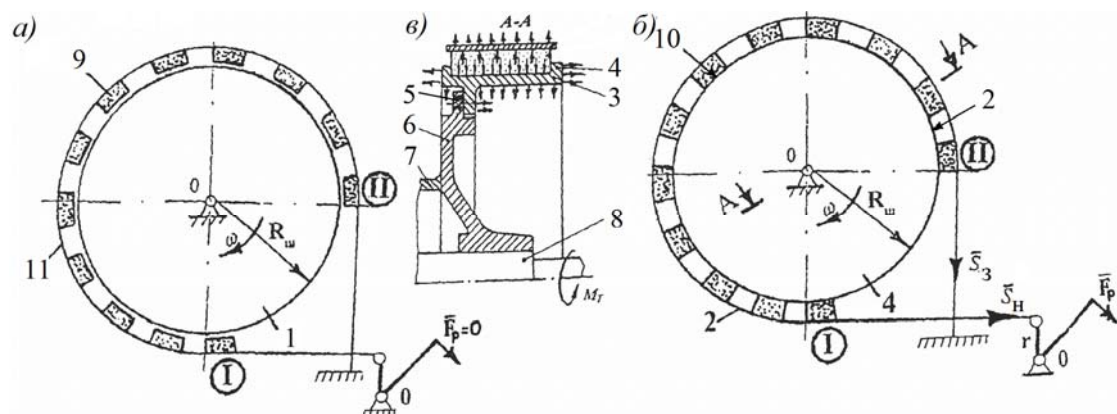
а, б, в – Кінематична схема серійного СКГ з розімкненими (а) і замкнутими (б) ФВ (в): 1, 2, 3, 4, 5 – ГШ, робоча і неробоча поверхні ободу, реборди і кріпильний виступ; 6, 7 – фланець барабана; 8 – підйомний вал; 9, 10 – ФН з робочою поверхнею; 11 – ГС з набігаючою (I) і збігаючою (II) гілками; S_H , S_3 – натяги набігаючої і збігаючої гілок ГС; M_T – гальмовий момент; F_p – зусилля робочого; ω – кутова швидкість ГШ; R_w , r – радіуси: робочої поверхні ободу ГШ і кривошипу колінчастого вала
